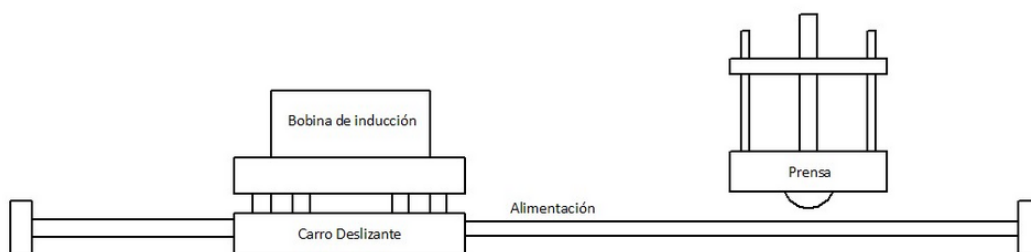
Esquema de soldadura por inducción. (48)
